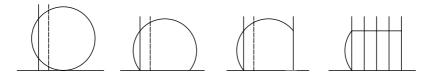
Схемы круглопильных станков для распиловки бревен и брусьев: a — однопильный с подачей на тележке; δ — станок с двумя пильными валами; ϵ — многопильный с подачей бревна цепным конвейером с упорами; ϵ — многопильный с подающими вальцами
